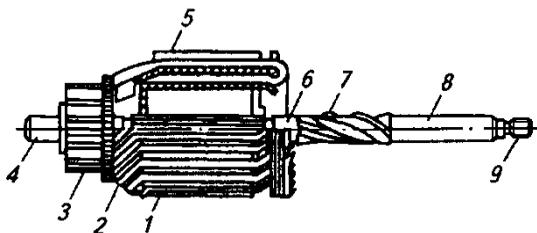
Места основных дефектов якоря стартера СТ-130 в сборе:
